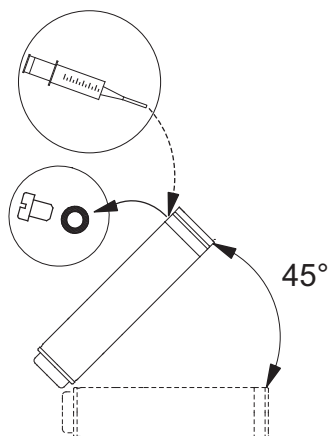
Posizione del motore durante il riempimento – MS6 e MS 6000
